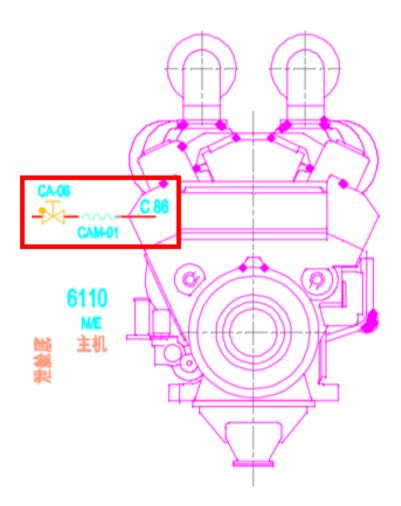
Muestra de válvulas sobre plano. Fuente: Planos de la sala de máquinas.
